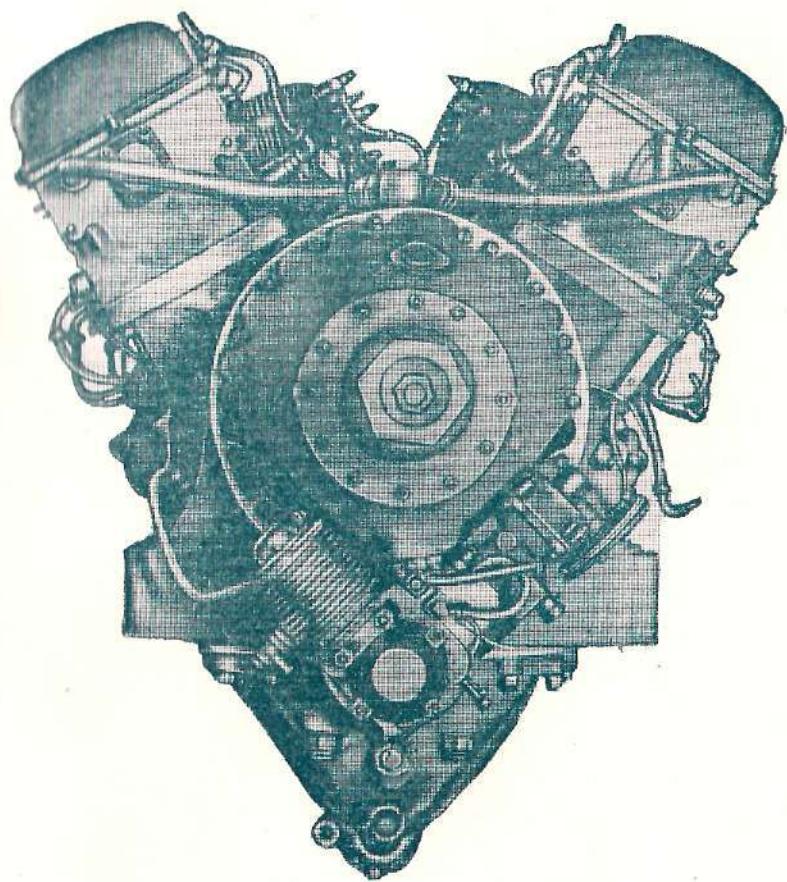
Вид мотора АМ-38 со стороны вала редуктора.
